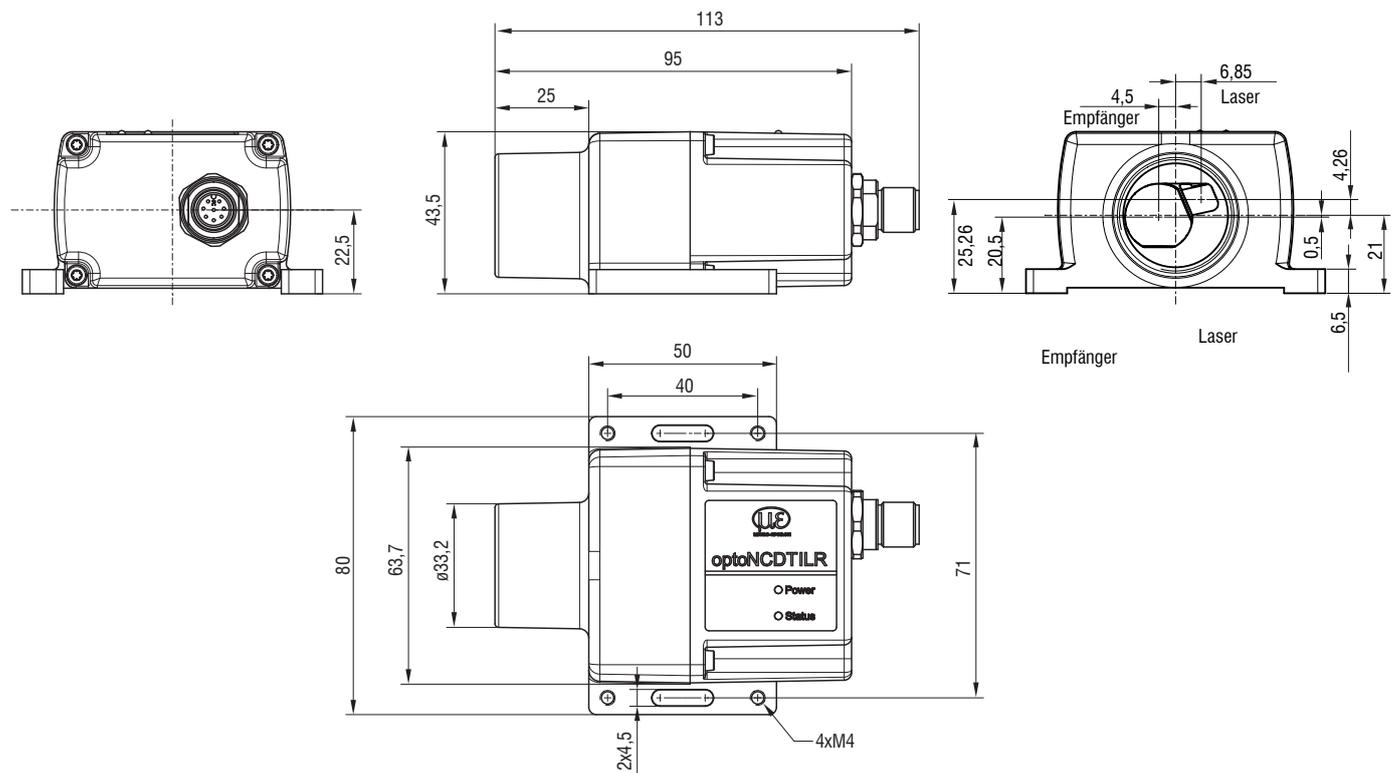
Maßzeichnung optoNCDT ILR3800-100, Abmessungen in mm
